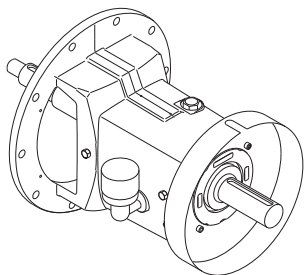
Корпус подшипников с системой постоянного уровня масла
